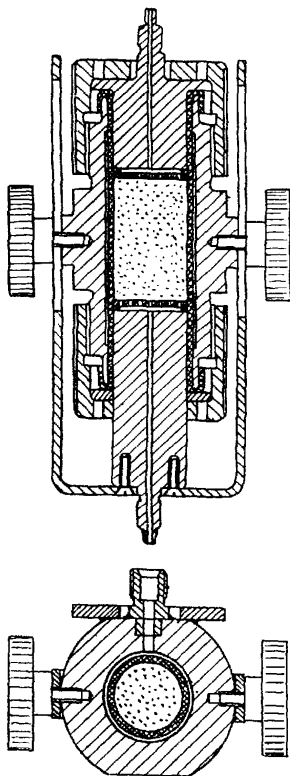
Конструкция быстрого съемного кернодержателя для образцов стандартного размера
